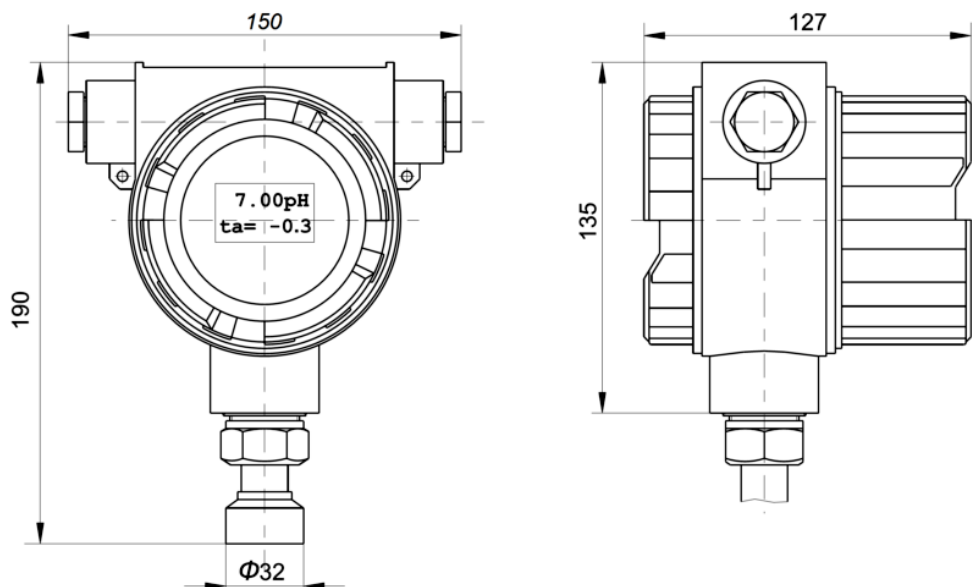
Габаритные и монтажные размеры рН-метра рН-4101 в корпусе "И"
